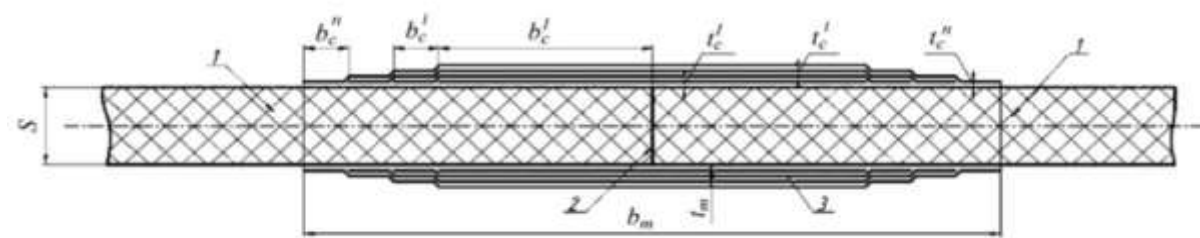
Конструктивна схема стикового (пазового) формованого з'єднання одношарових в'язей без оброблення крамок:
